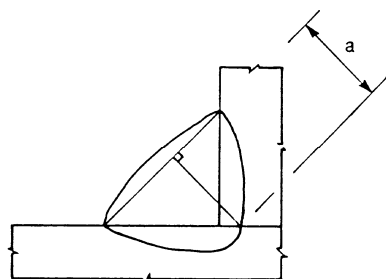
Espessura de um cordão de soldadura com elevada penetração
